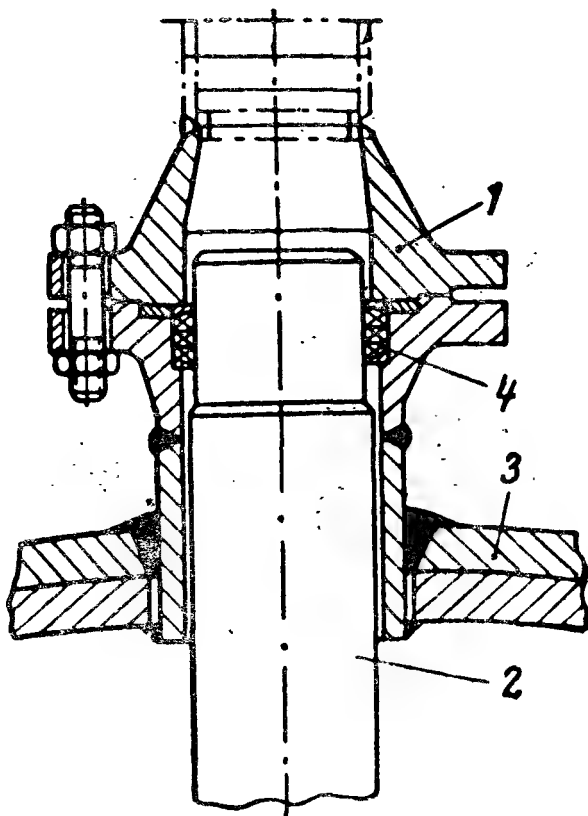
Ввод пара в корпус подогревателя. 1 — паропровод от турбины; 2 — труба к охладителю пара; 3 — корпус подогревателя (верхнее днище), 4 — сальниковое уплотнение
